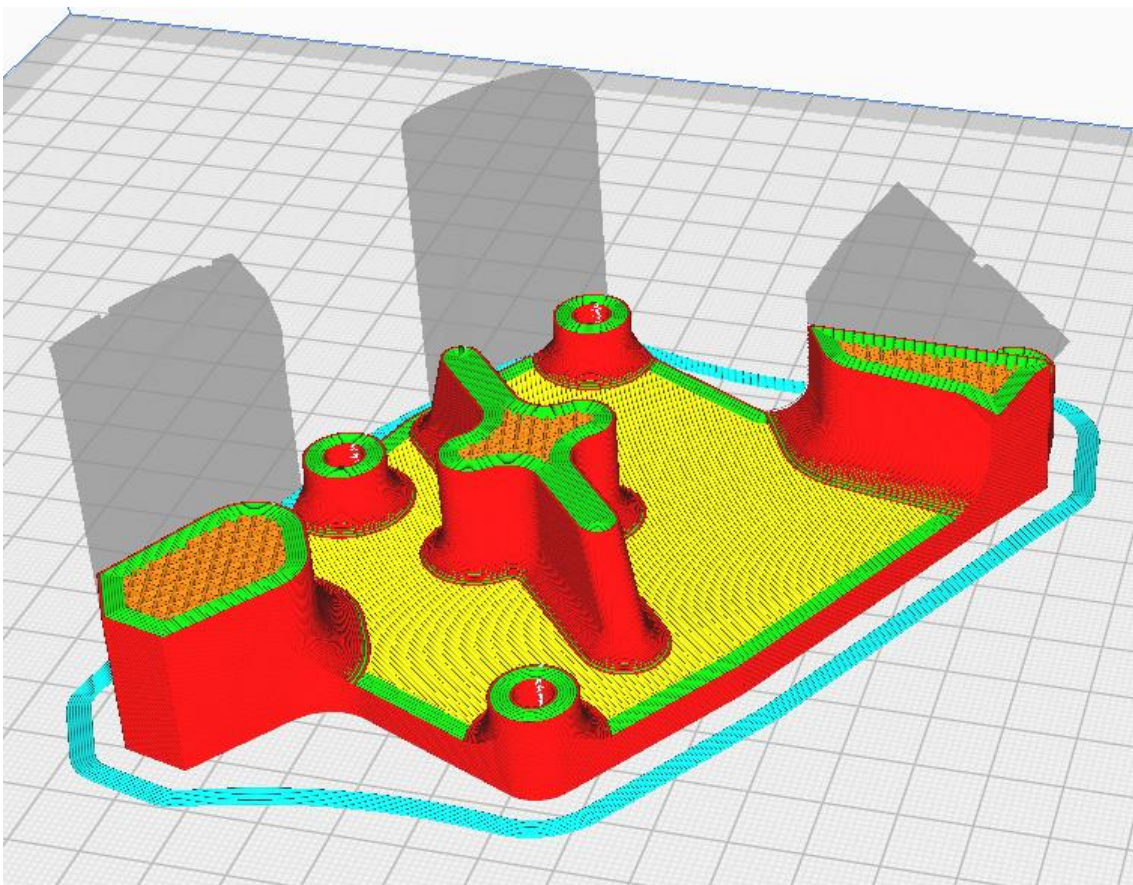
Vista módulo 2 del utillaje para pieza 4 en el laminador de Ultimaker Cura
